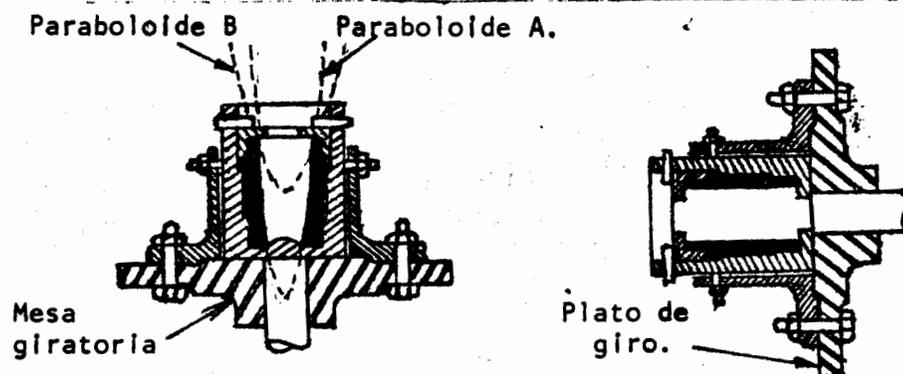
Método de colado centrífugo real para cilindros de motor radial.
